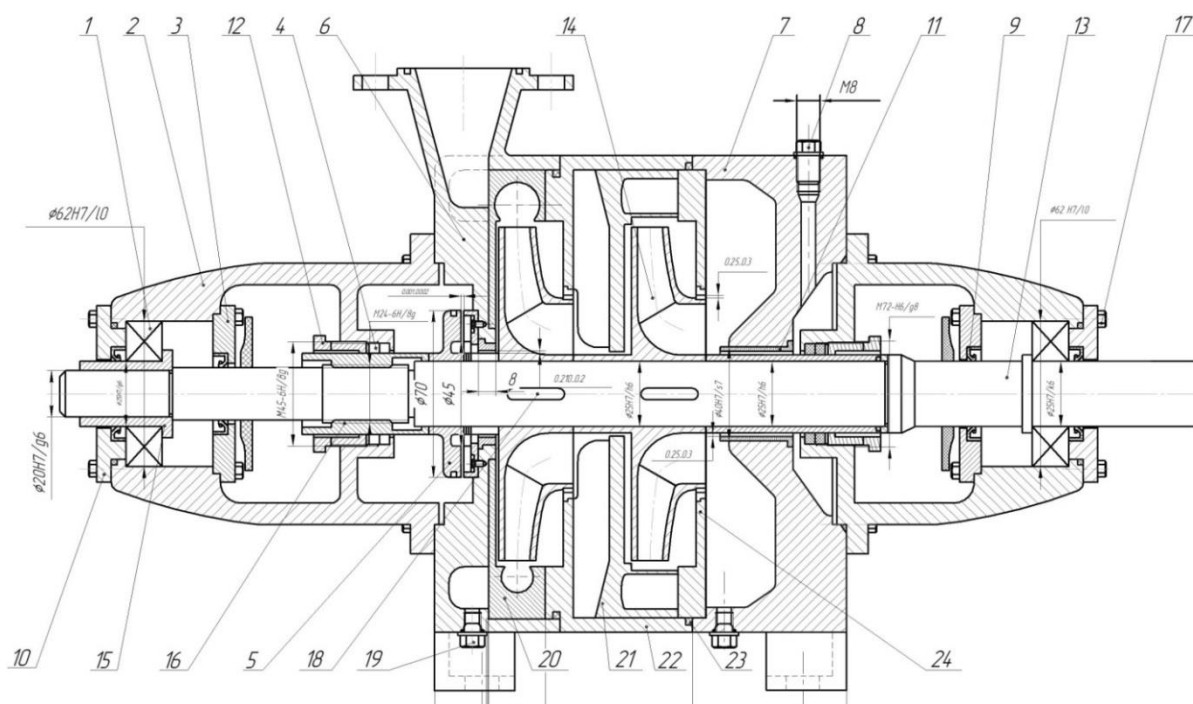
Общий вид конструкции проектируемого насоса: 1 – подшипник; 2 – кронштейн; 3 – крышка внутренняя; 4 – набивка сальниковая; 5 – пята гидравлическая; 6 – корпус; 7 – крышка корпуса; 8, 17 – болт; 9 – манжета; 10 – крышка подшипника; 11, 16 – втулка; 12 – крышка сальника; 13 – вал; 14 – рабочее колесо; 15 – отбойник; 23 – уплотнение.
